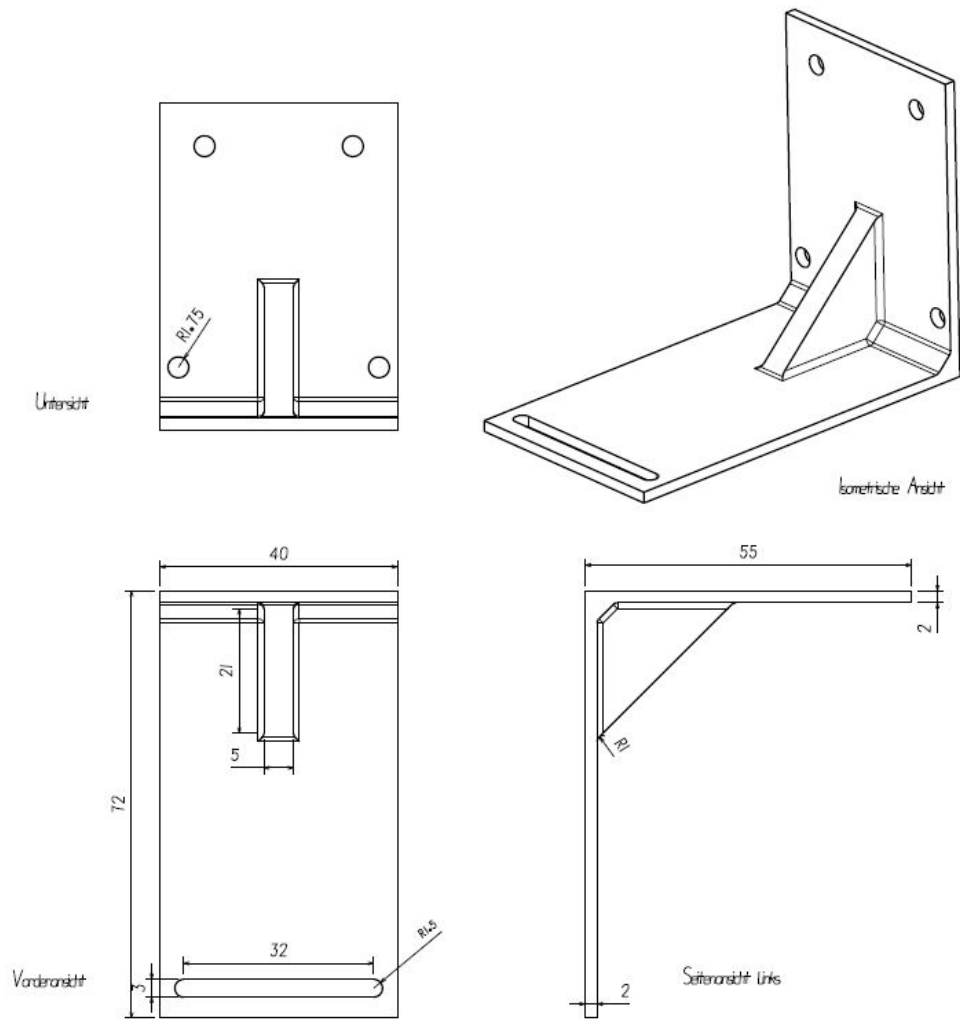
Abb. XIV Technische Zeichnung von dem Lese-/Schreibkopfständer
